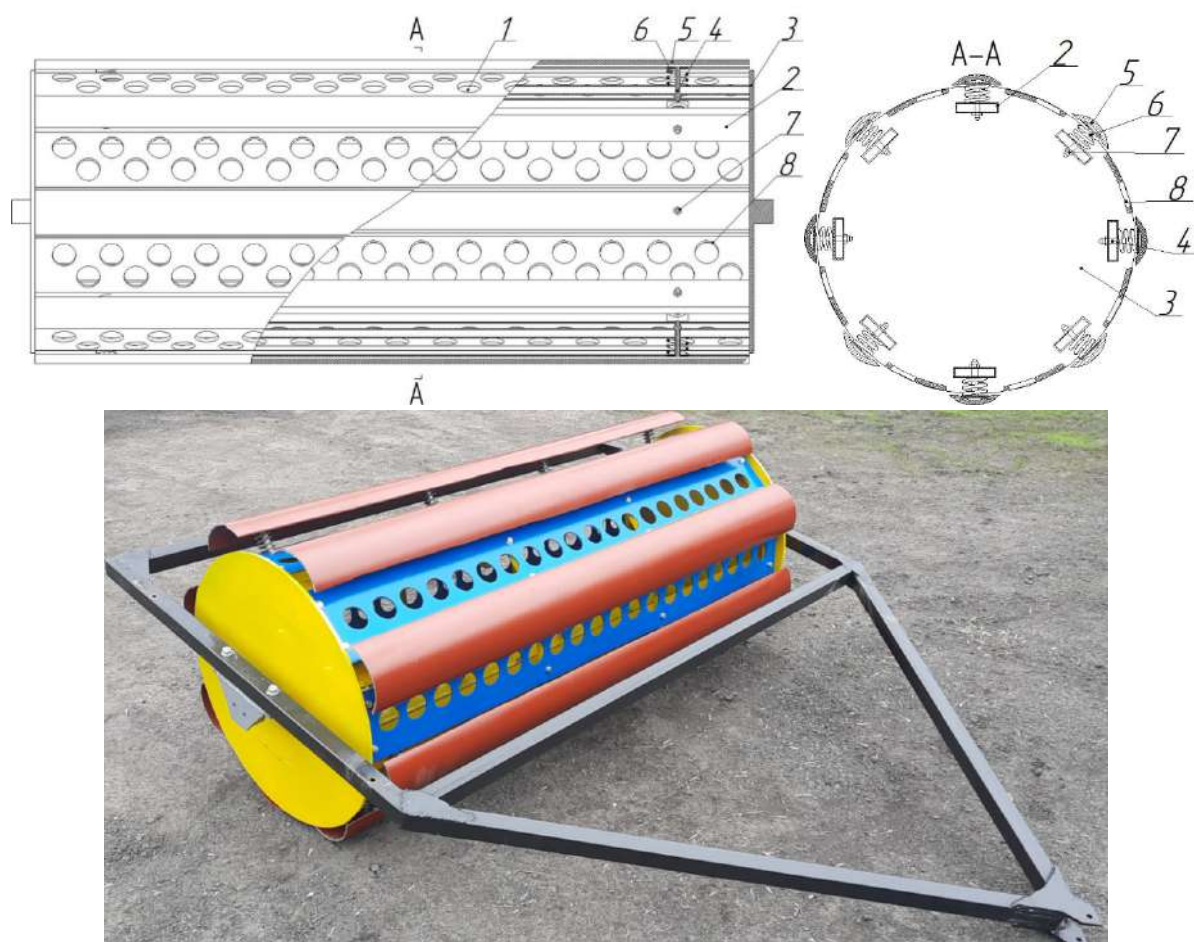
Пружинно-волновой каток: 1 - пластины образующей цилиндра; 2 - ребра; 3 - вертикальные диски; 4 - шпильки; 5 - уплотнители; 6 – пружины сжатия; 7 - самоконтрящиеся гайки; 8 - отверстия
